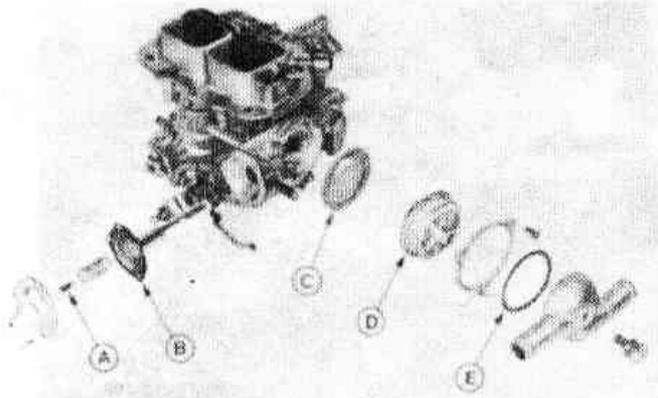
Вакуумная диафрагма (B) и регулировочный винт (A). Внутренний теплоизоляционный щиток (C), корпус (D) и прокладка (E) (Разд.27)
